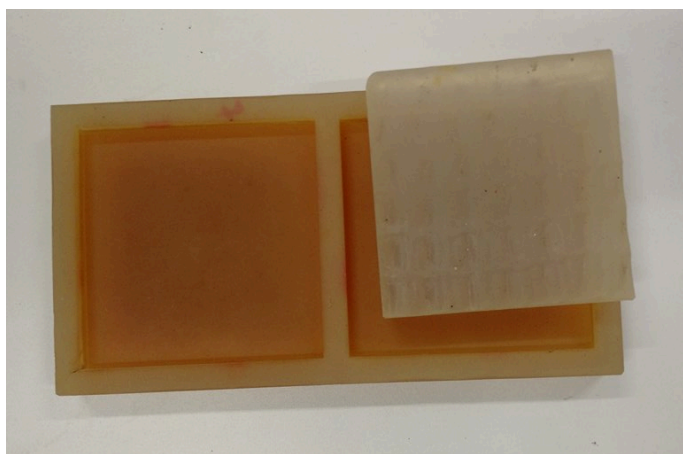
Molde de silicone com quadrados de 10x10 mm.
